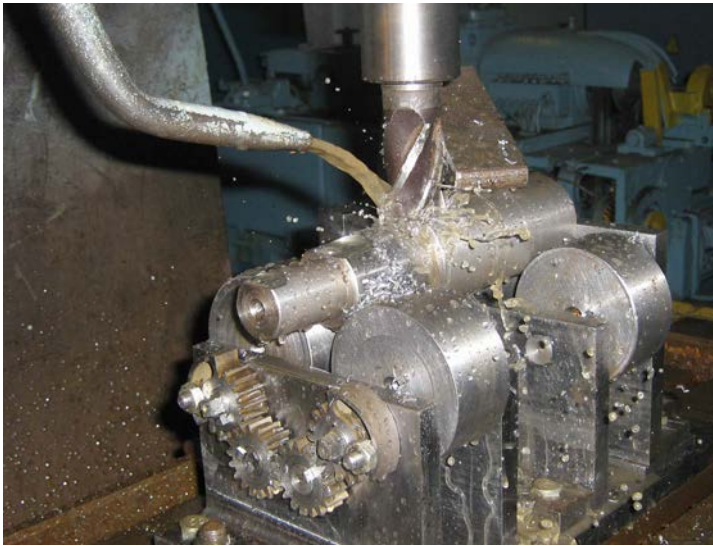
Фрезерування лиски на вертикально-фрезерному верстаті мод. 6P13Ф3 при установленні заготовок на запропоновану базуючу призму
